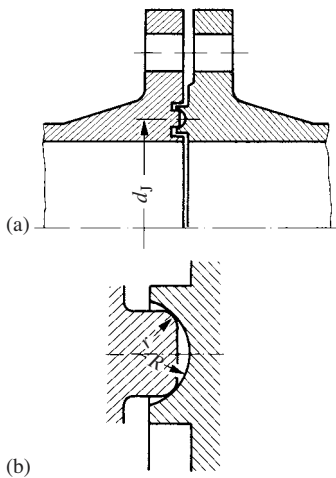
Brides DILO: (a) ensemble; (b) détail du joint.
